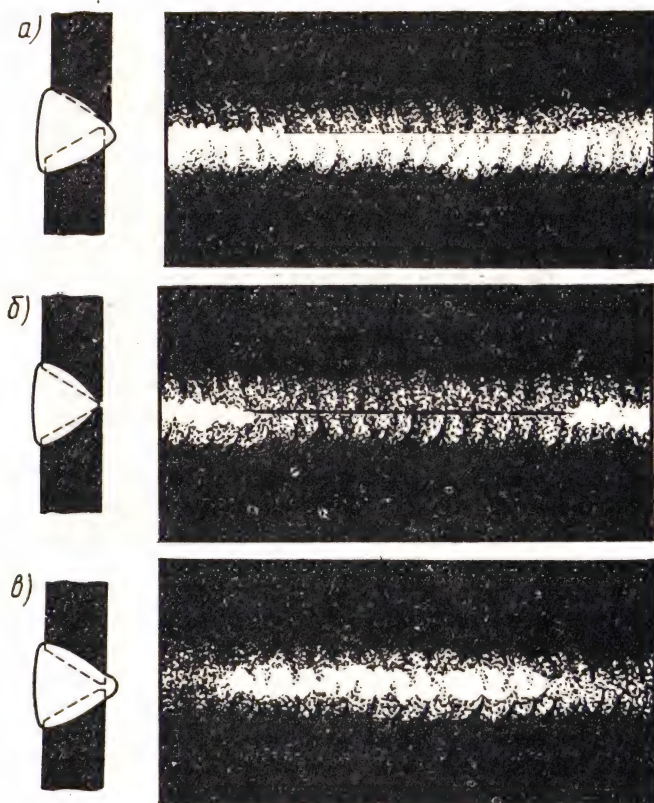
Схема и рентгеновский снимок сварного шва со смещением стыкуемых кромок и непроваром по кромке (а), с непроваром в корне (б) и чрезмерным проваром (в)
